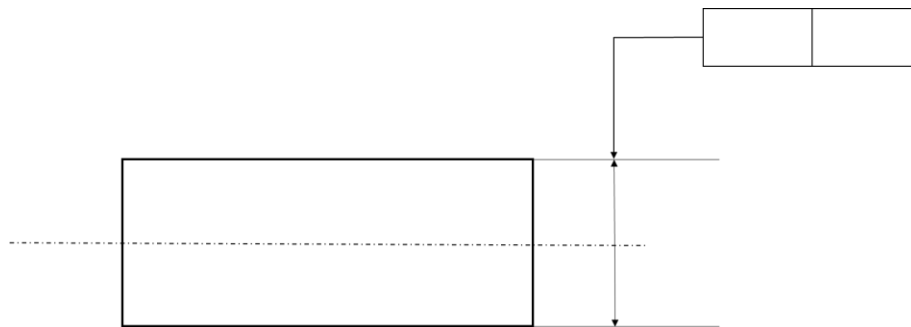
Colocación de tolerancia sobre la línea de cota (paralela a la línea de cota)
